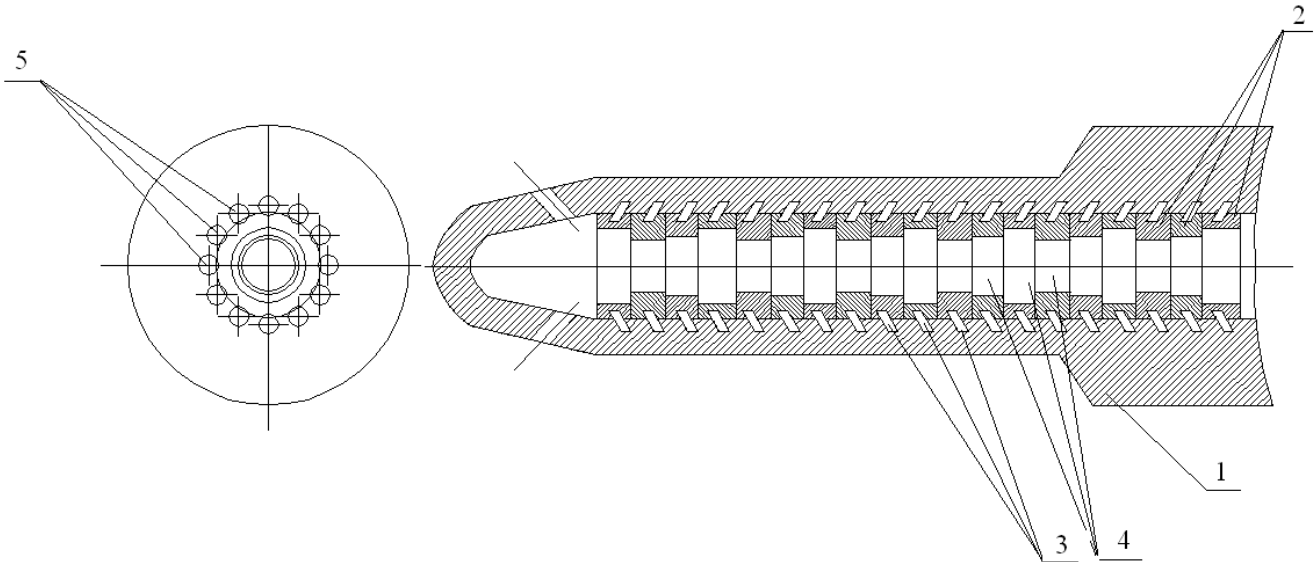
Модифікатор структури важкого палива: 1 – корпус розпилювача; 2 – шайби; 3 – канали рельєфу особливого профілю на корпусі розпилювача зовнішньому боці шайб та; 4 – перемінний прохідний діаметр шайб; 5 – вхід каналів особливого профілю.
